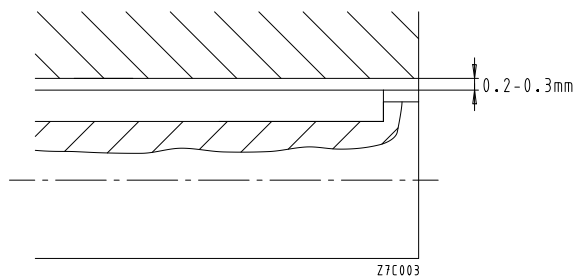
Допуск между шпоночной канавкой и призматической шпонкой
